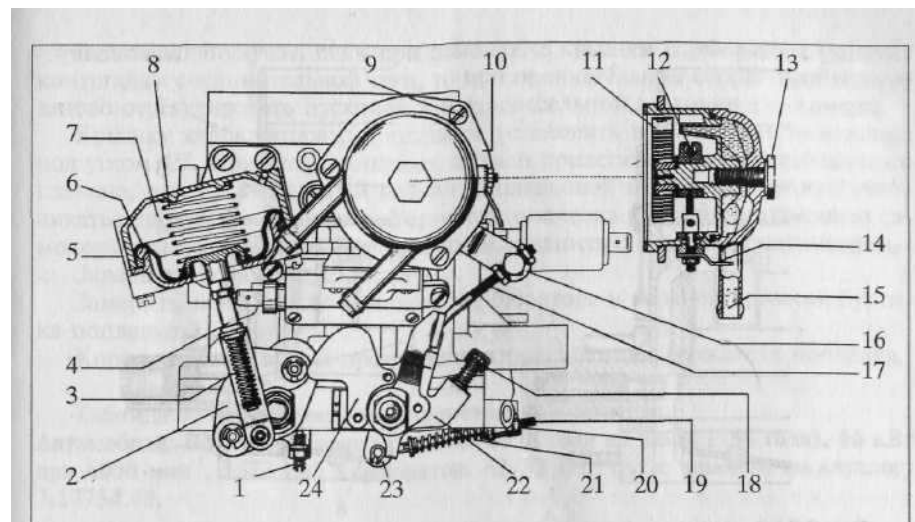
Карбюратор Solex с нисходящим потоком и с последовательным включением камер 32/32 DIDTA. Схематический разрез механизма пневмопривода 2-й камеры, а также комбинированного подогрева автоматического пускового устройства: 1 — упорный винт; 2 — рычаг привода заслонки 2-й камеры; 3 — пружина штока; 4 — шток механизма пневмопривода; 5 — корпус пневмопривода 2-й камеры; 6 — вакуумная мембрана; 7 — мембранный механизм пневмопривода 2-й камеры; 8 — пружина; 9 — цилиндрический винт; 10 — фиксирующее кольцо; 11 — биметаллическая пружина; 12 — спираль электронагревательного элемента; 13 — стяжной винт; 14 — электрическая присоединительная клемма; 15 — штуцер подвода жидкости из системы охлаждения; 16 — рычаг пускового устройства; 17 — соединительная тяга пускового устройства; 18 — установочный винт дроссельной заслонки; 19 — тяга привода ускорительного насоса; 20 — регулировочный винт производительности ускорительного насоса; 21 — пружина на тяге привода ускорительного насоса; 22 — рычаг привода дроссельной заслонки; 23 — передаточный рычаг ускорительного насоса; 24 — кулачок блокировки 2-й камеры.
